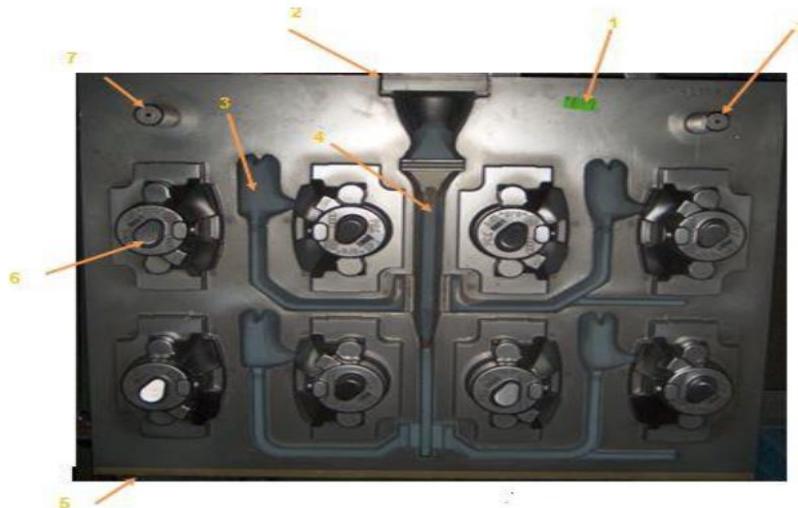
Exemplo de placa molde e zonas críticas de inspeção
